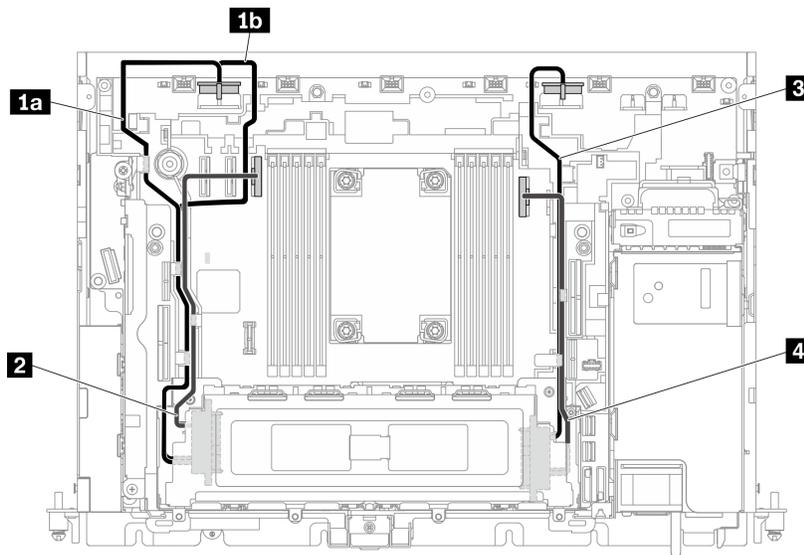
Kabelführung für drei oder vier 7-mm-Laufwerke (NVMe)
